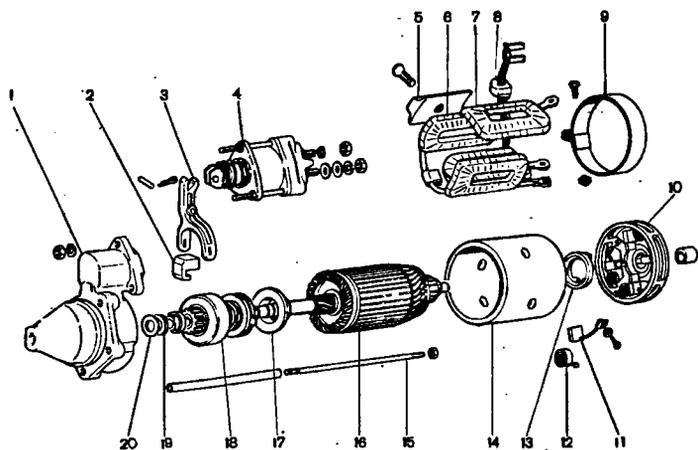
Детали стартера СТ-221: 1 - крышка стартера со стороны привода; 2 - резиновая заглушка; 3 - рычаг привода; 4 - тяговое реле; 5 - полюс статора; 6 - серийная обмотка статора; 7 - шунтовая обмотка статора; 8 - резиновая заглушка; 9 - защитная лента; 10 - крышка со стороны коллектора; 11 - щетка; 12 - пружина щетки; 13 - тормозной диск крышки; 14 - корпус; 15 - стяжная шпилька; 16 - якорь; 17 - ограничитель хода шестерни; 18 - обгонная муфта с шестерней привода; 19 - упорная шайба; 20 - регулировочная шайба
